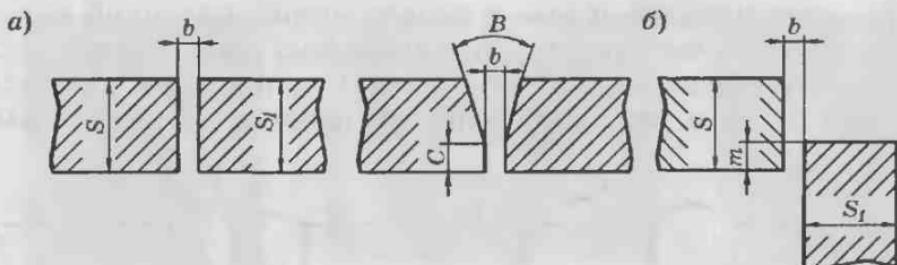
Элементы геометрической формы подготовленных кромок под сварку стыковых (а), угловых (б) соединений:
